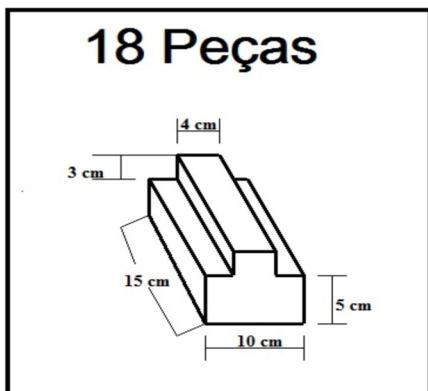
e 11 - Medidas e foto da peça em madeira maciça, utilizada para construção do pé direito.
